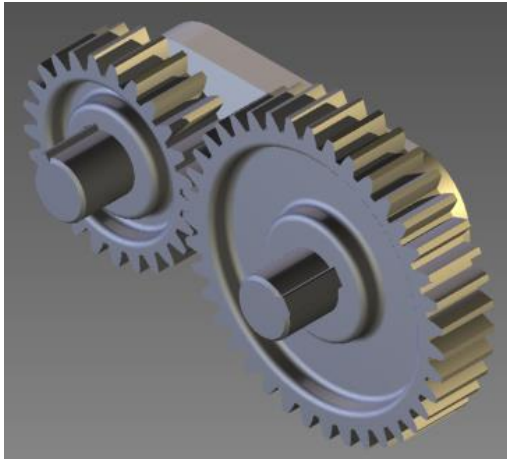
Engranajes cilíndricos, con dentado recto y helicoidal.
